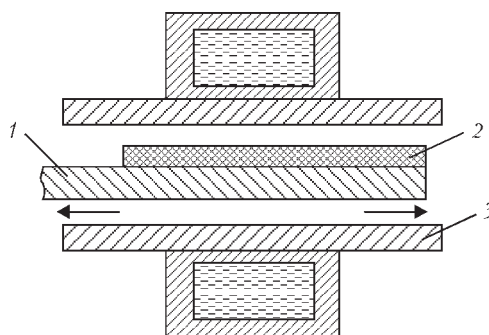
Схема индукционной наплавки: 1 — наплавленная деталь; 2 — порошкообразная шихта; 3 — индуктор (стрелками указано направление горизонтальной вибрации)
